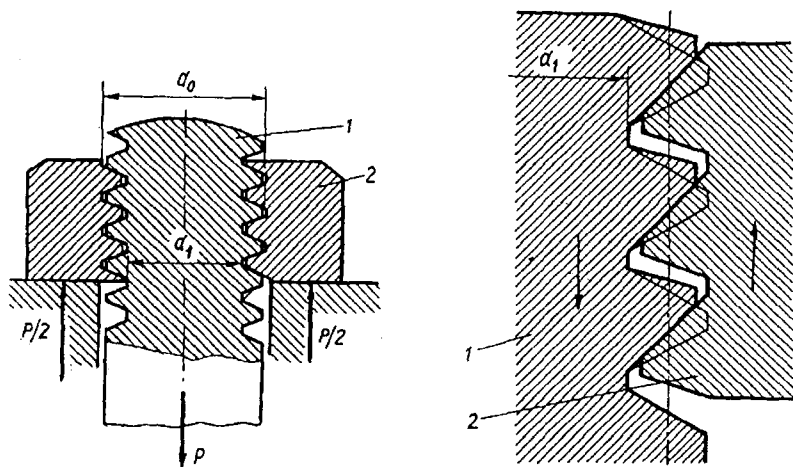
Болтовое соединение под нагрузкой: 1 – болт; 2 – гайка.
